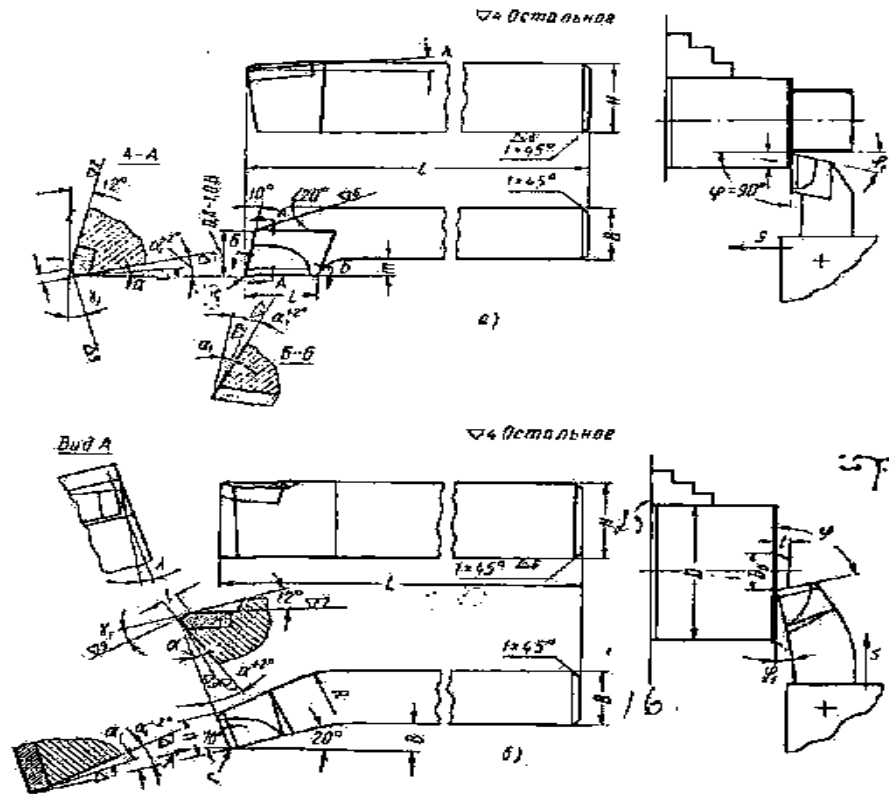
Токарные резцы, оснащенные пластинками твердого сплава
